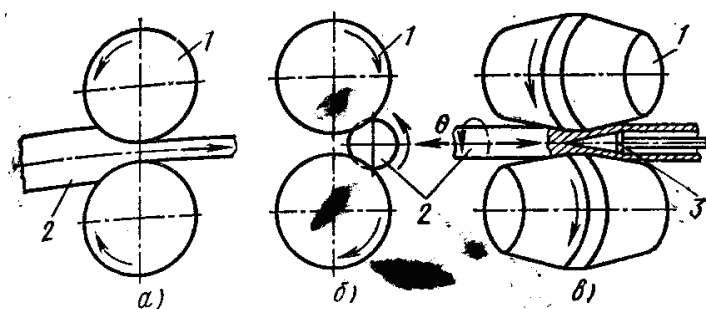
Основные виды прокатки: 1-валки; 2-заготовка; 3-оправка
